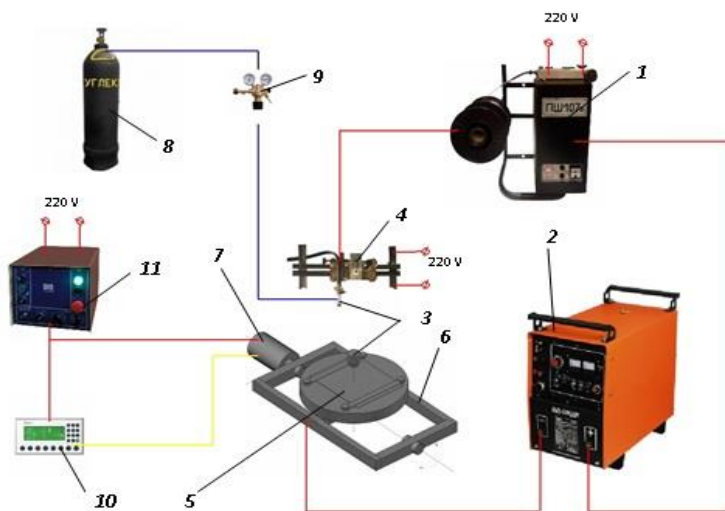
Структурна схема установки для наплавлення: 1 – півавтомат зварювальний; 2 – джерело живлення; 3 – зварювальний пальник; 4 – рухома станина; 5 – деталь що наплавляється; 6 – коливальний стіл; 7 – кроковий двигун; 8 – балон газовий; 9 – редуктор газовий; 10 – пульт керування; 11 – блок керування. Червона – силова магістраль; Блакитна – газова магістраль; Жовта – магістраль програмування
